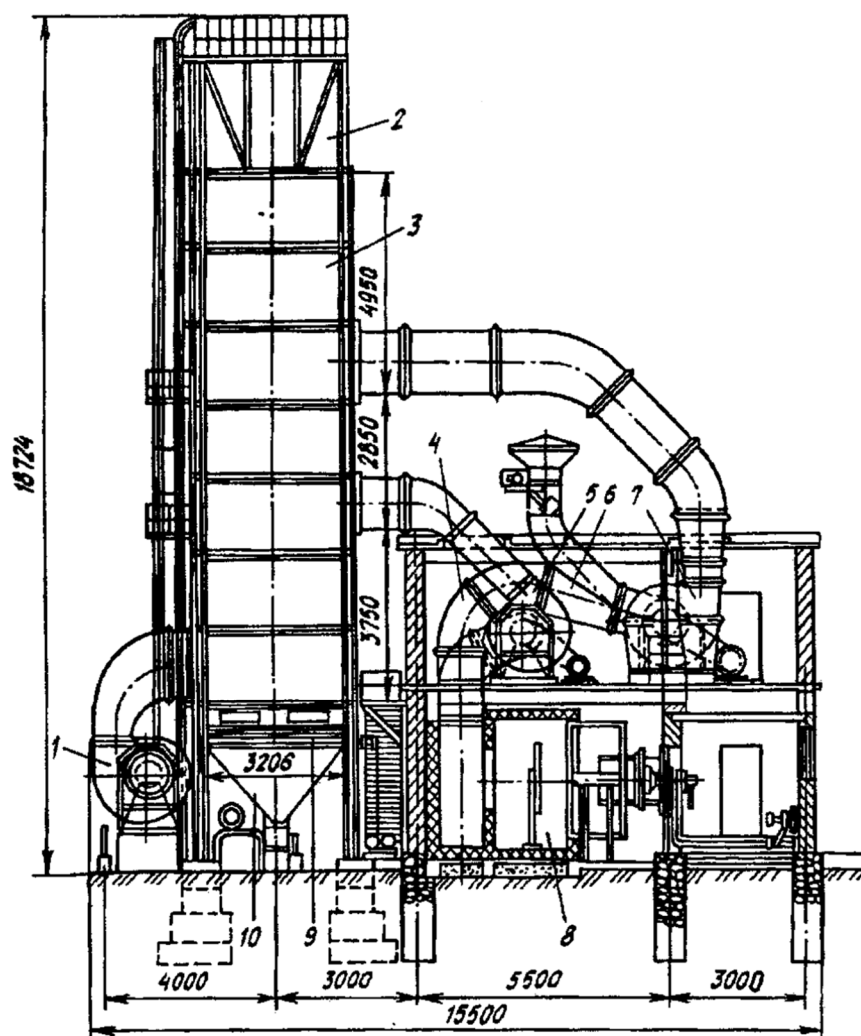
Зерносушарка ДСП–32от: 1 – вентилятор охолоджувальної зони; 2 – надсушильний бункер; 3 – сушильні шахти; 4 – всмоктувальний повітропровід вентилятора другої зони; 5 – вентилятор другої зони; 6 – всмоктувальний повітропровід вентилятора першої зони; 7 – вентилятор першої зони; 8 – топка; 9 – випускний механізм; 10 – підсушильний бункер
